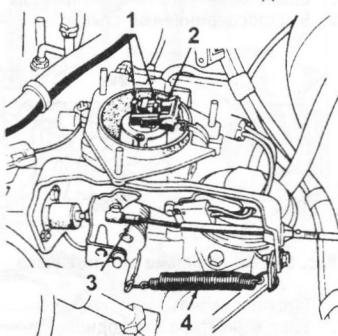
Чтобы отсоединить разъем инжектора на автомобилях с СВКД, сожмите шпонки и поднимите
